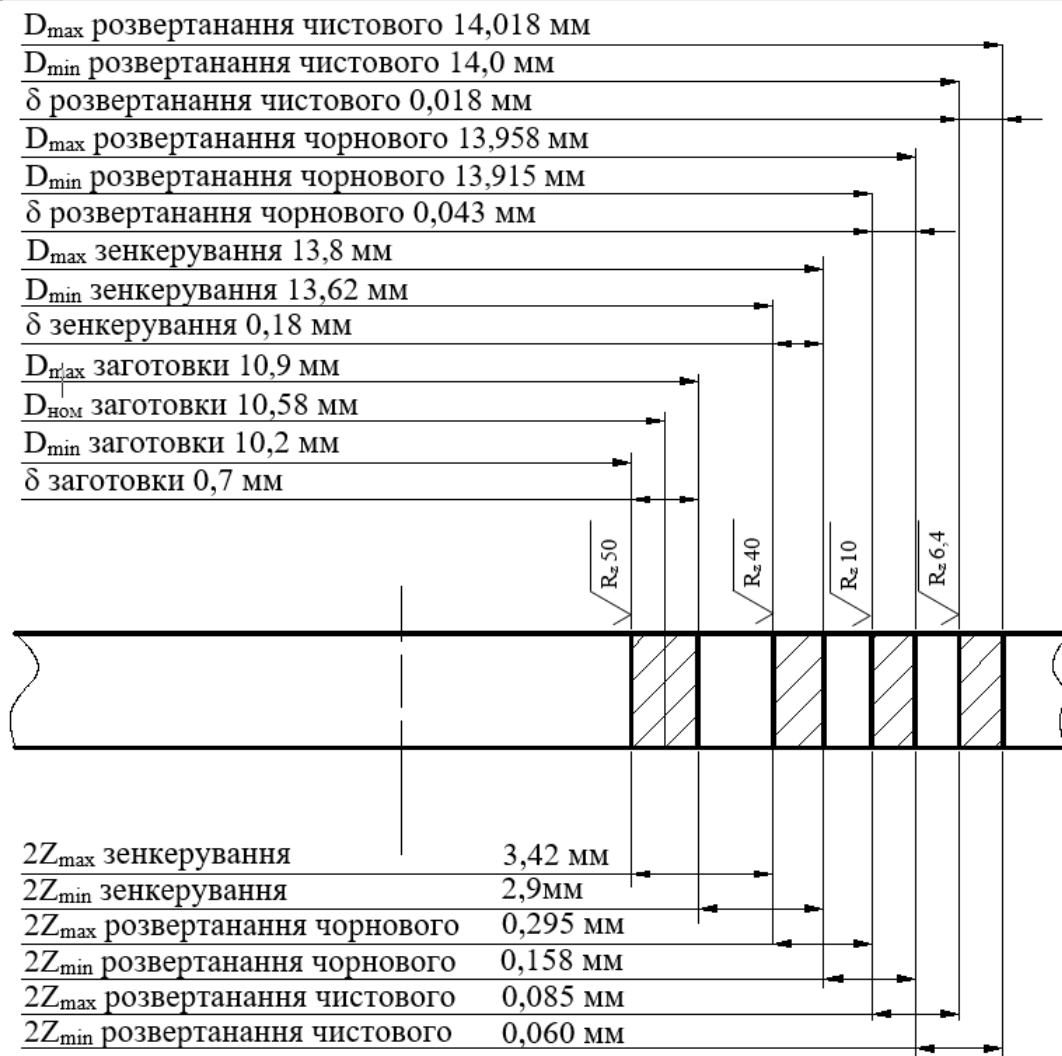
Схема розташування припусків на механічне оброблення
